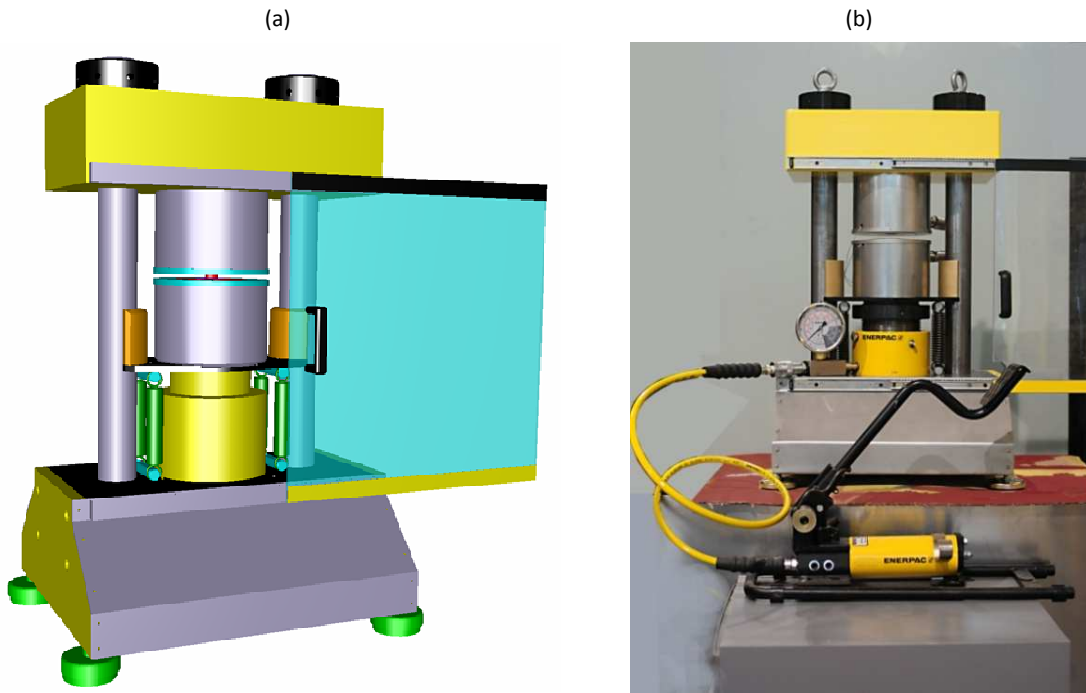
2. Dessin CAO (a) et photographie de la presse à enclumes (b)
